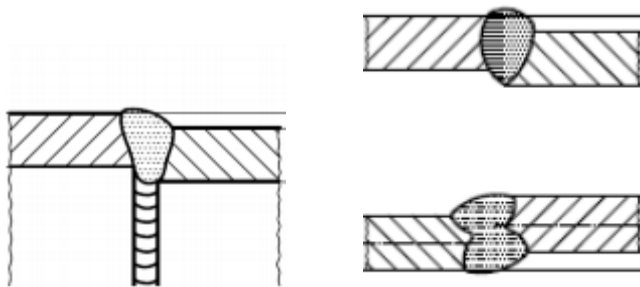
Défaut d'alignement d'un cordon de soudure (Réf.[R15])
